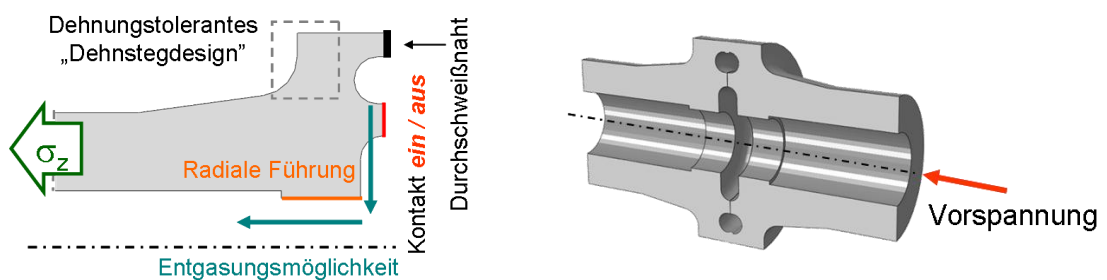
Querschnitt durch Laserschweißrundprobe
